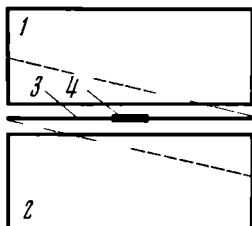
Барабан двухуголовочного видеомagnитofона: 1, 2 — верхняя и нижняя половины барабана; 3 — вращающаяся тарелка; 4 — видеоголовка
